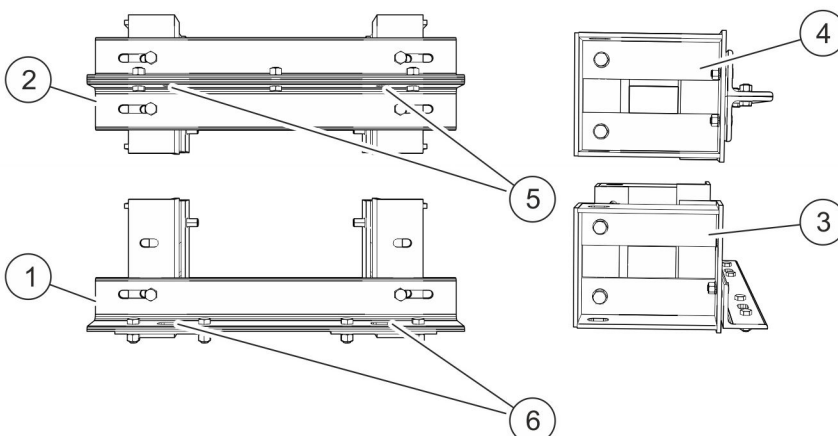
Alu-Winkel, Frontansicht und Seitenansicht
